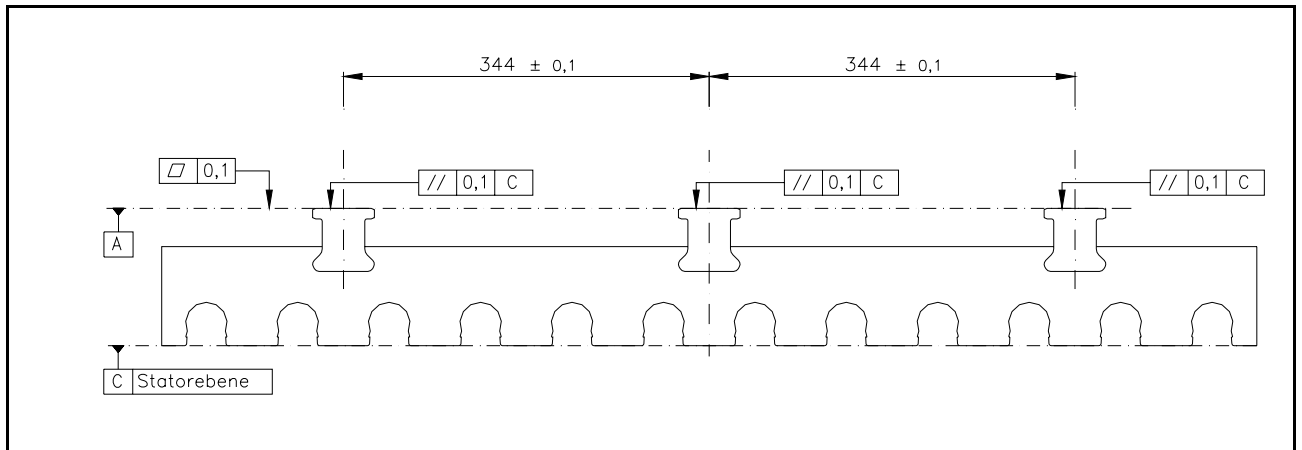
Befestigungsachsen des Statorpaketes (Seitenansicht)
